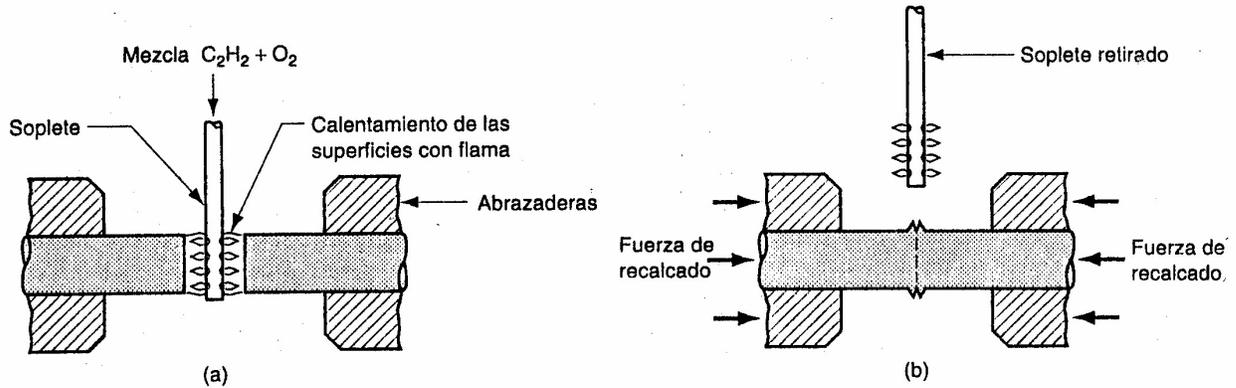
Una aplicación de soldadura con gas a presión: (a) calentamiento de las dos partes y (b) aplicación de presión para formar la soldadura.
